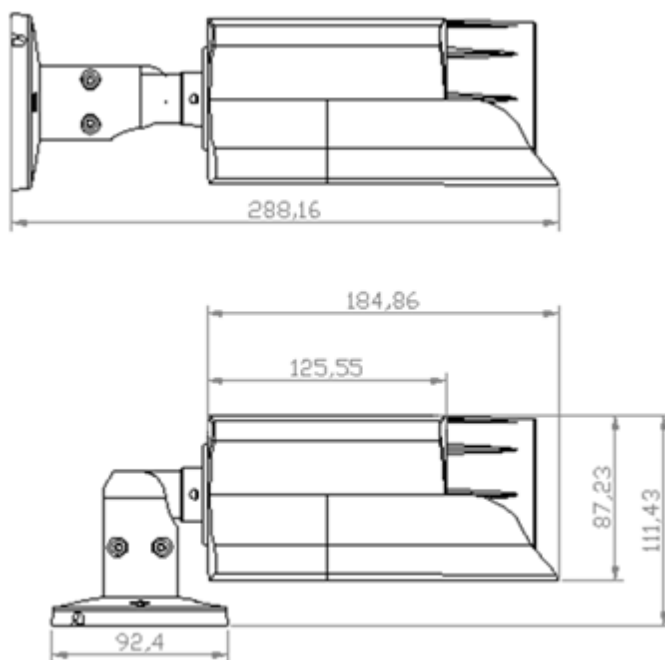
Габаритный чертеж видеокамеры ИВМ-501М.
